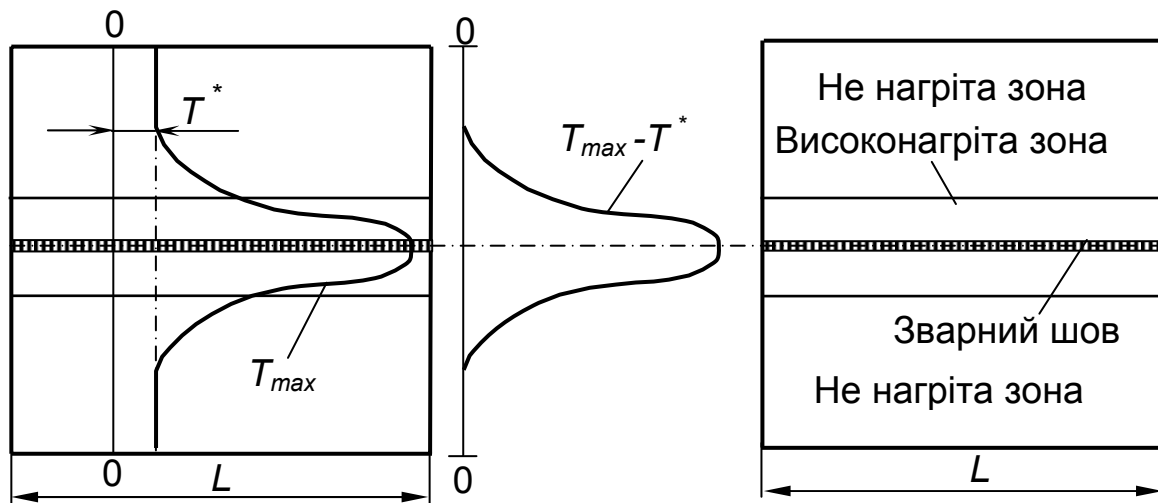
Схема нагрівання зварного з'єднання під час зварювання
